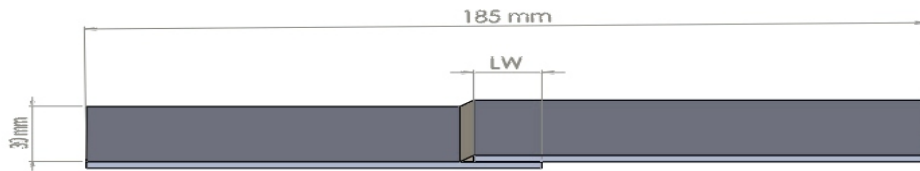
Assemblages soudés par MAG des éprouvettes 304L.
